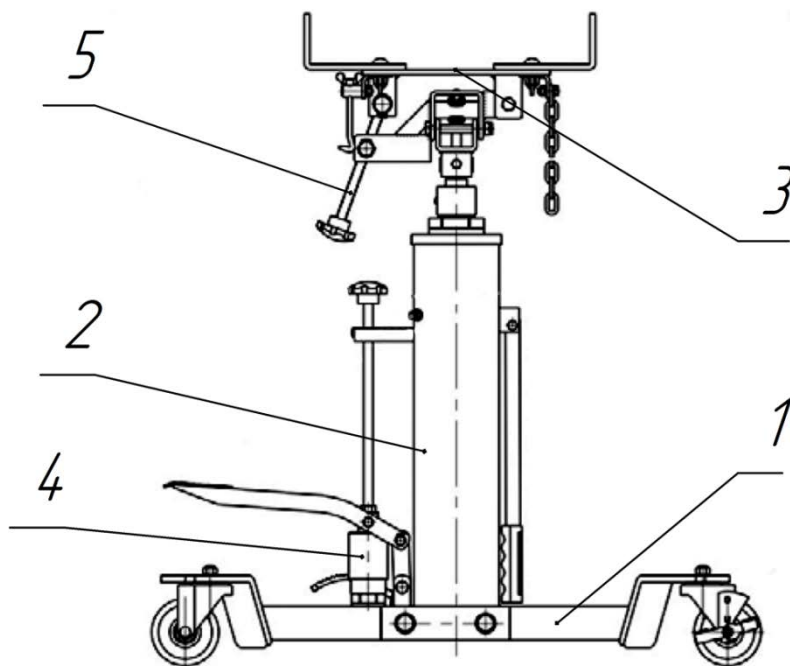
Пристрій для демонтажу – монтажу коробок передач: 1 – рухомий візок; 2 – гідрофікована стійка; 3 – ложе для коробки передач; 4 – гідропривід; 5 – фіксатор коробки передач.
